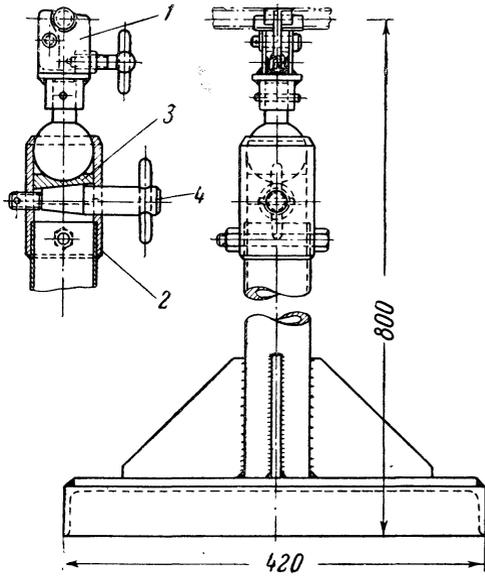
Поворотное устройство приспособления для сварки кольца моторамы.
